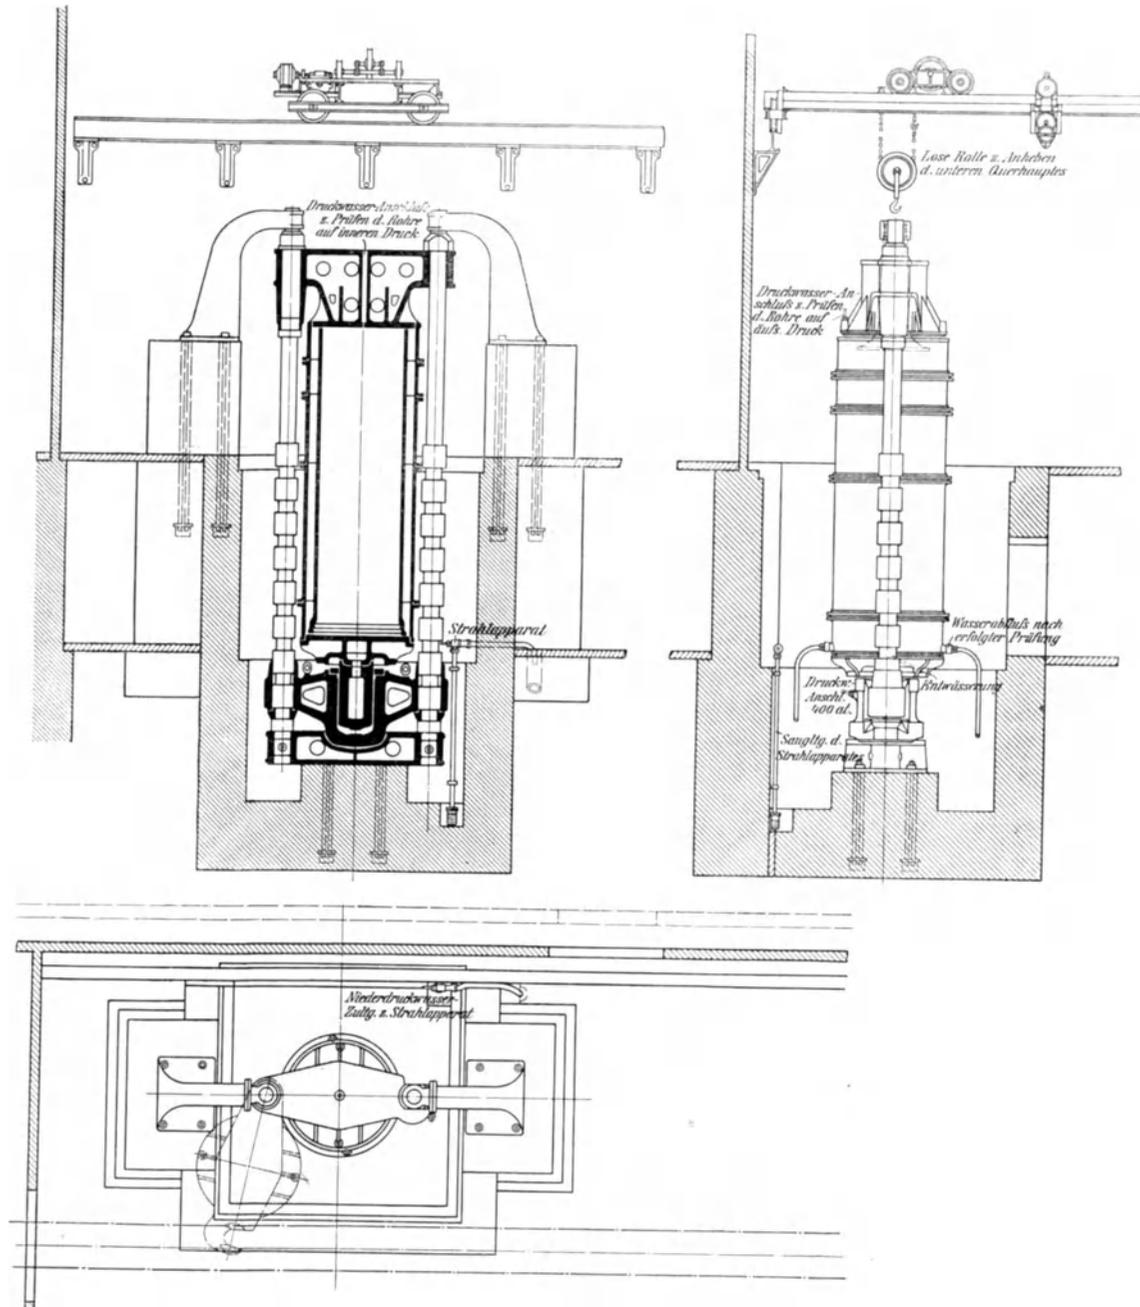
Rohrprüfungsmaschine von Borsig. A. Borsig-Tegel.
